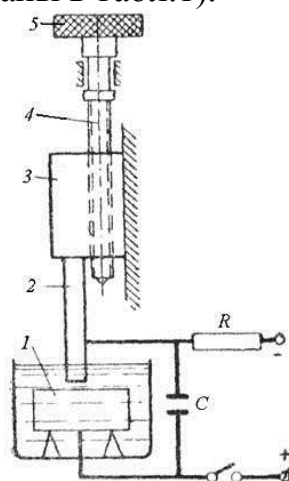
Схема станка для электроискровой прошивки отверстий
